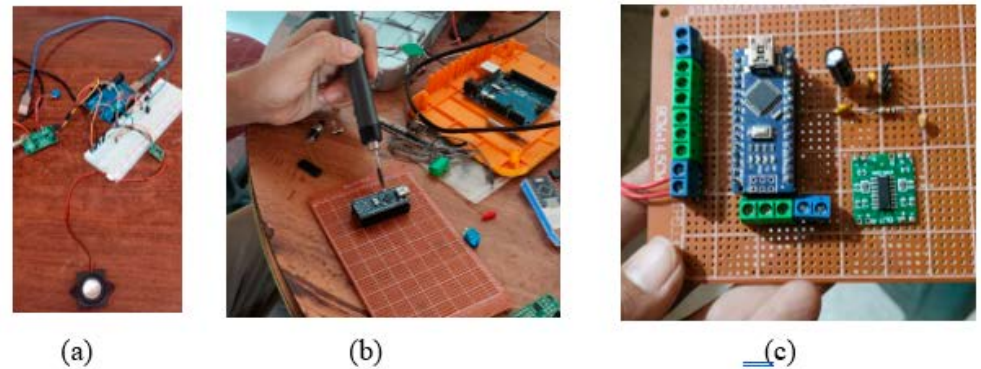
(a) Prototipo inicial en protoboard, (b) Proceso de soldadura y ensamblaje, (c) Circuito final montado
